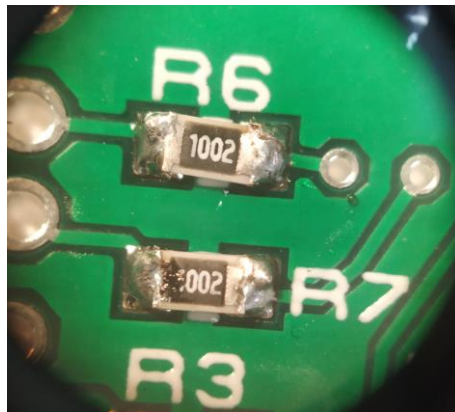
Resistencias R6 y R7 soldadas en PCB
